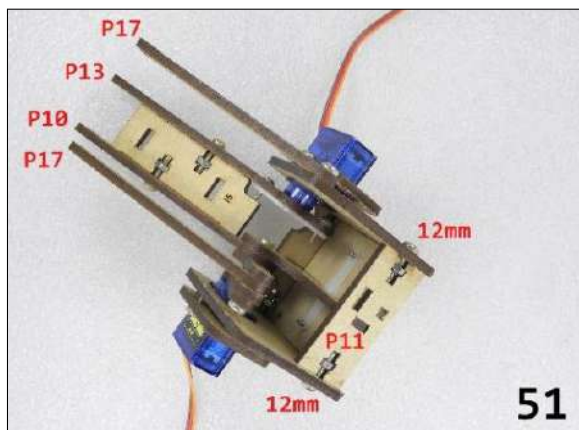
Montagem da estrutura cotovelo e ombro: nono passo do guia didático de montagem do motor em MDF.
